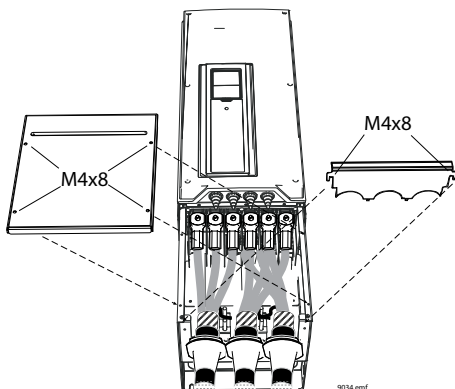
Recolocar a placa de fixação dos cabos e a tampa
